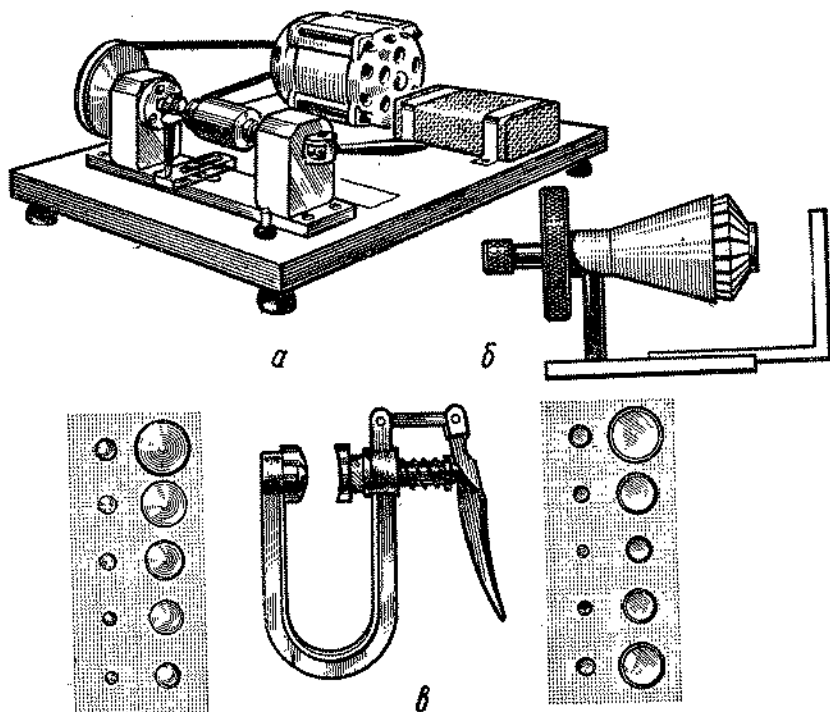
Станок и приспособления для обточки и вставки стекол:
